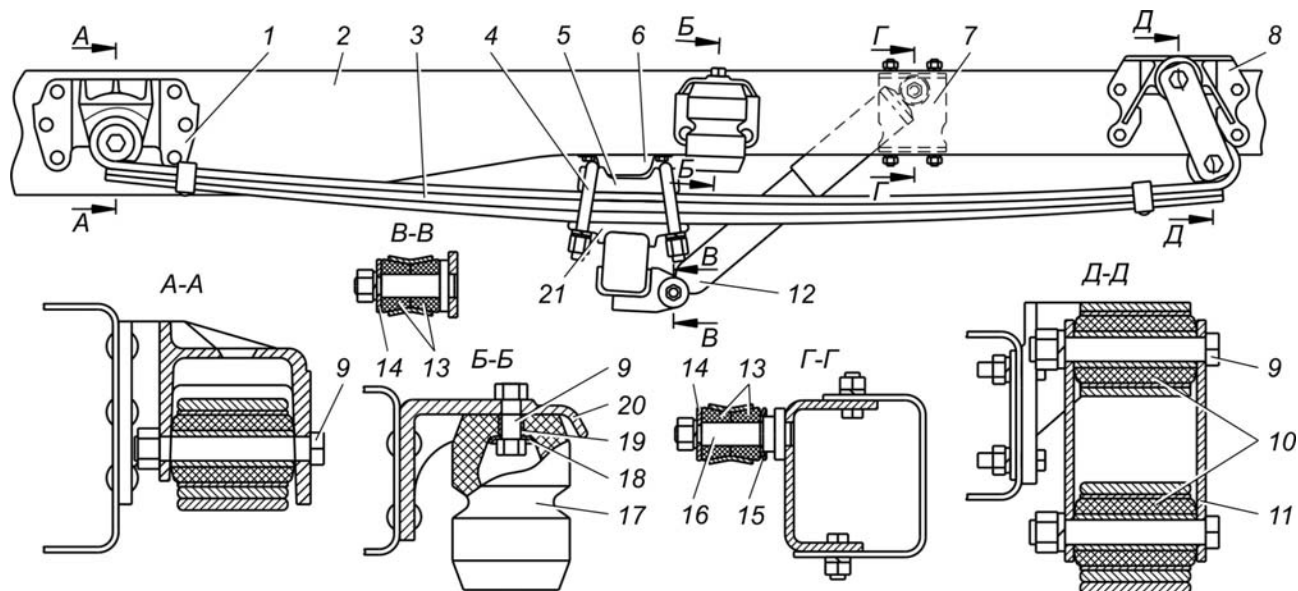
Задняя подвеска автобусов типа 4x2 и автомобилей ГАЗ-32214: 1, 7, 8 и 20 – кронштейны; 2 – лонжерон рамы; 3 – рессора; 4 – стремянка; 5 – накладка; 6 – буфер; 9 – болт; 10 – резинометаллические шарниры; 11 – серьга; 12 – амортизатор; 13 – резиновые втулки; 14, 15 и 18 – шайбы; 16 – палец; 17 – буфер; 19 – втулка; 21 – подушка
